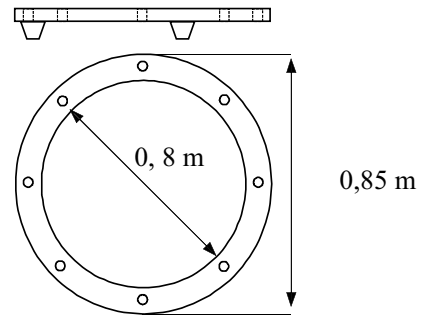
Sistema anelar para molde de fixação dos eletrodos no solo.
